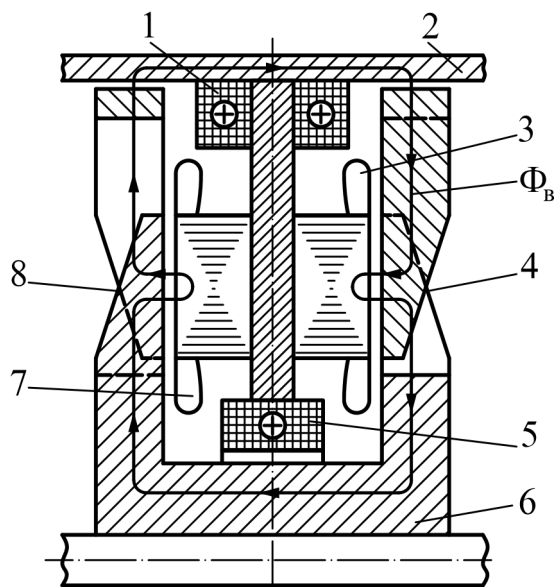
Торцева двопакетна БСМ із внутрішніми якорями
